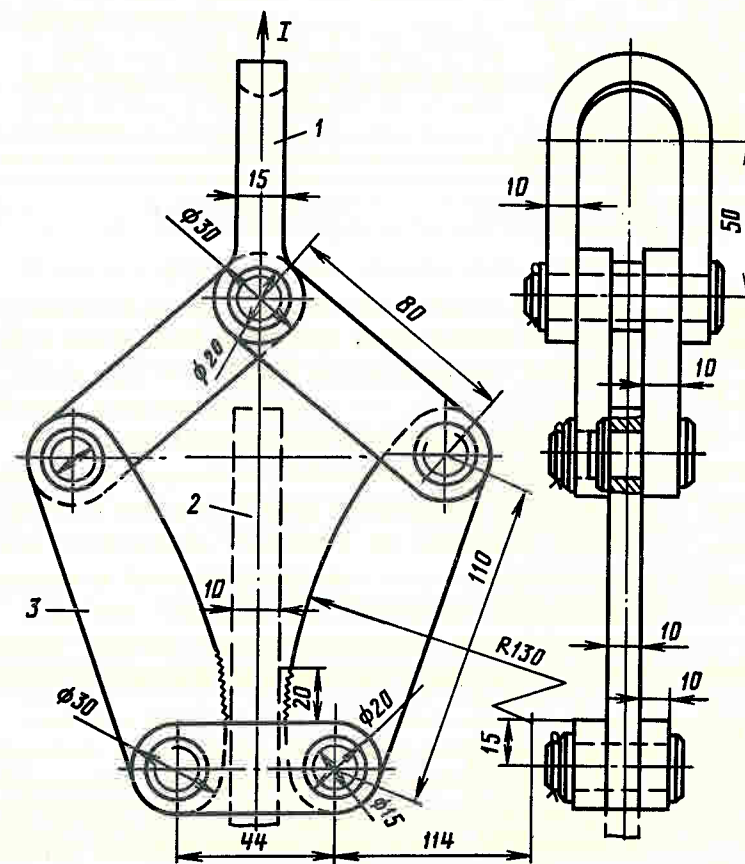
Рычажное приспособление для выдергивания клиньев полюсов ротора гидрогенератора:
